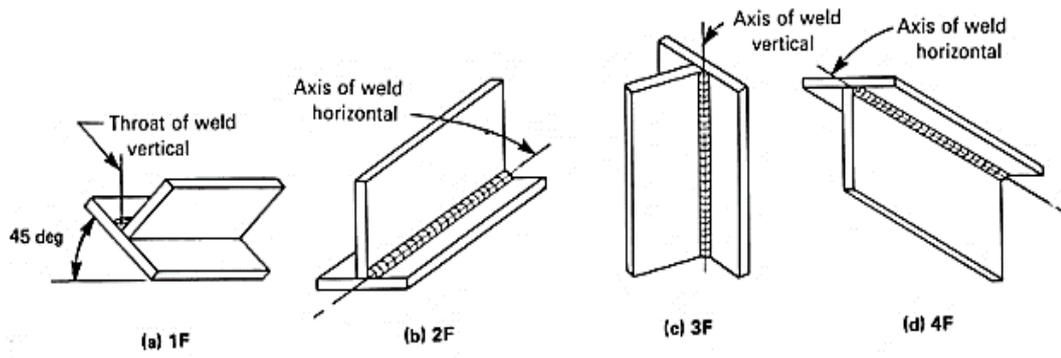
Posiciones de soldadura para placas en filete.
